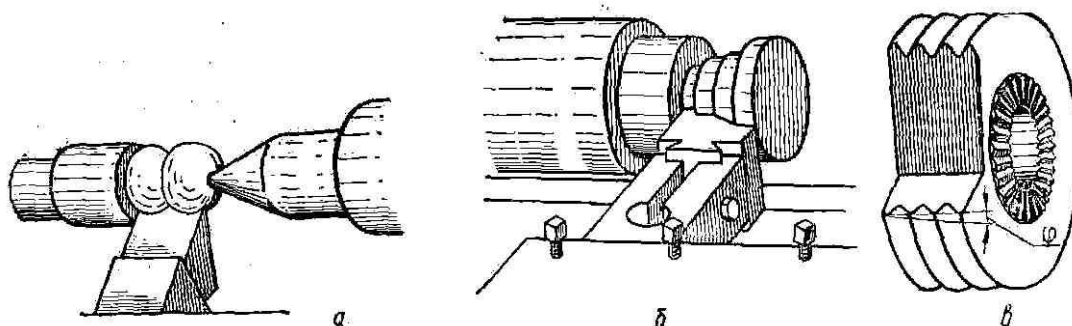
Схемы обработки поверхности вращения фасонным резцами
